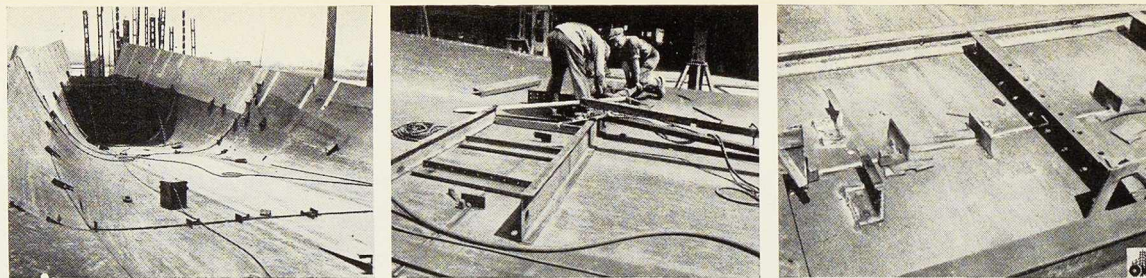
à 18. Disposition initiale des tôles de quille à recouvrement avant découpage au chalumeau des surlongueurs. — Exécution du soudage à l'arc des joints bord à bord préparés par oxy-coupage au chalumeau. — Joint bord à bord préparé pour le soudage à l'arc (chantier J. Boel).
